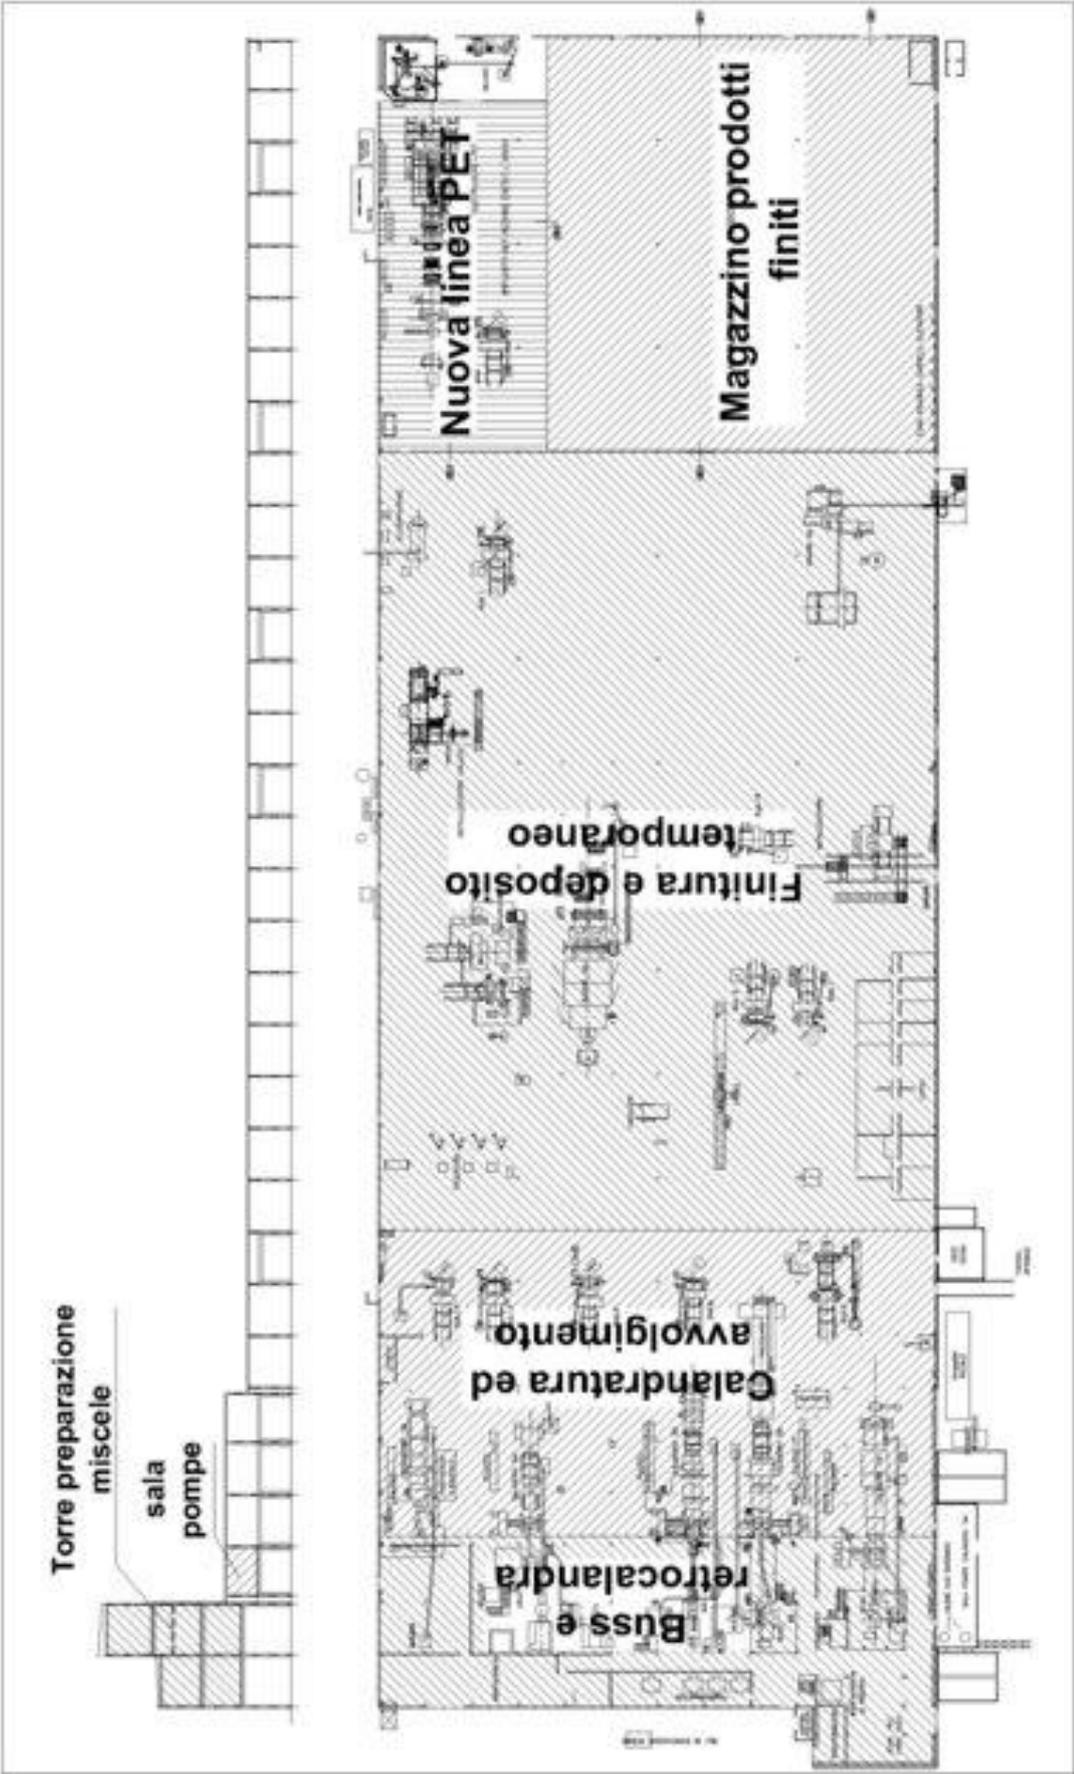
Plant-layout di uno stabilimento dedito alla produzione di PVC
